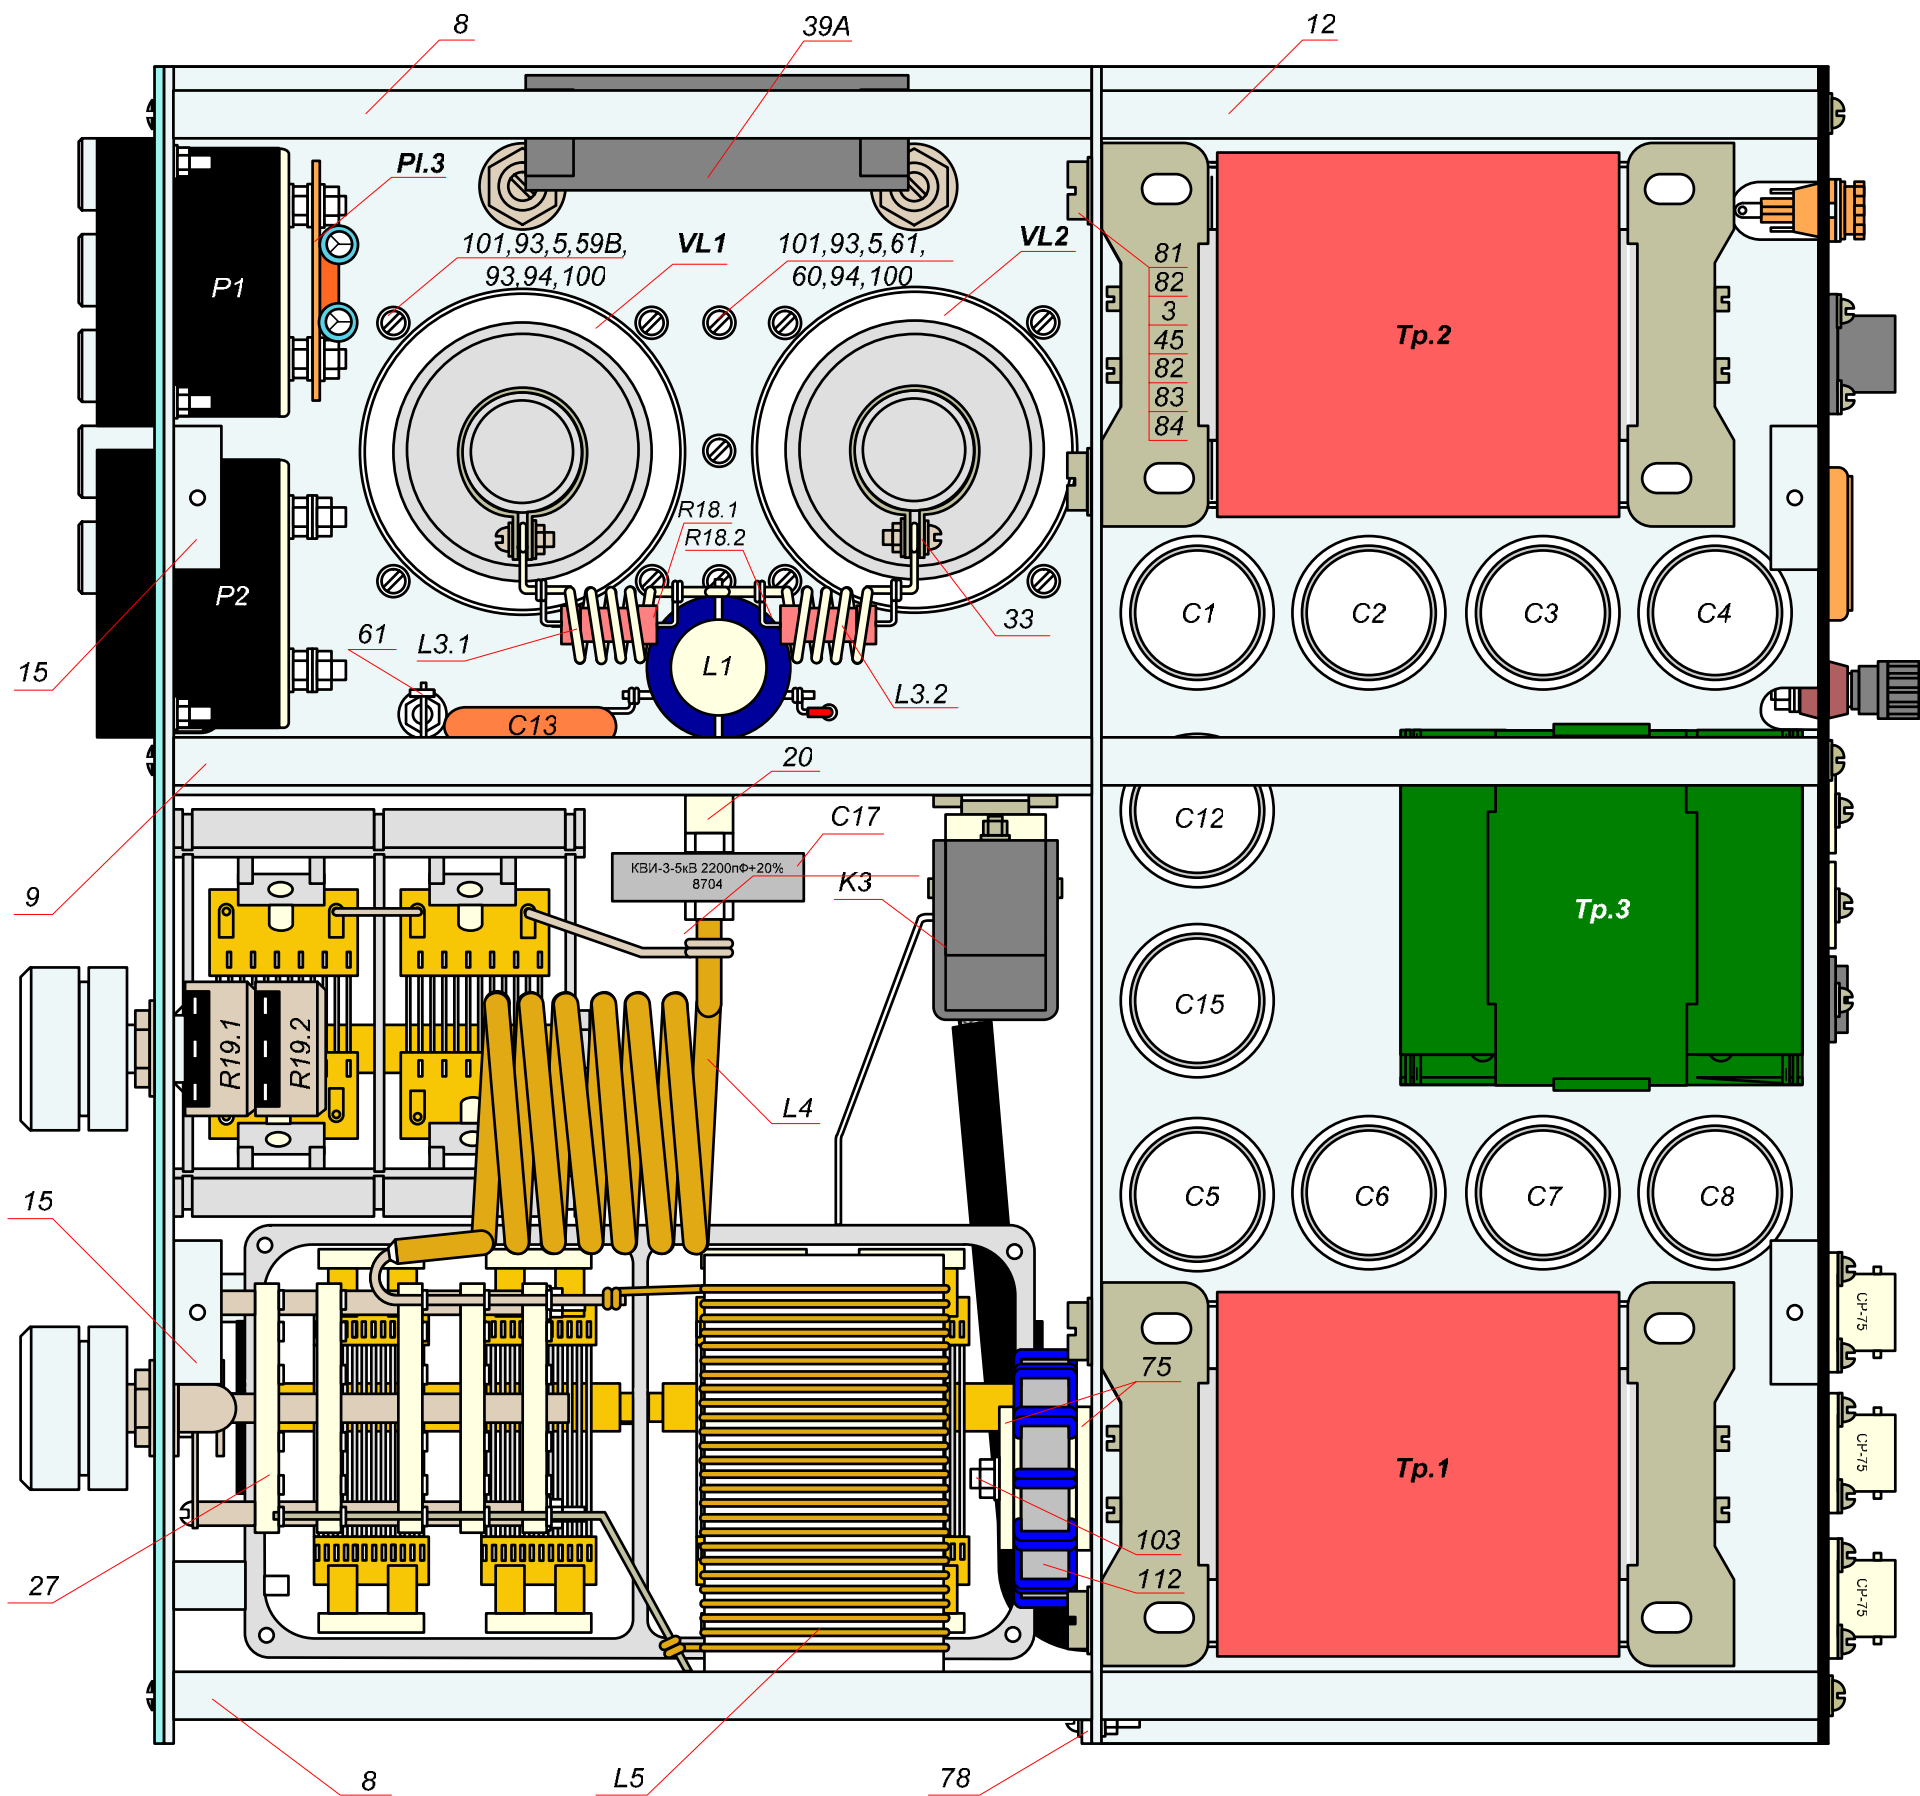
ВМ. Сборочный чертёж усилителя DVA-300ВМ. Вид сверху со снятыми верхней и нижней крышками.
